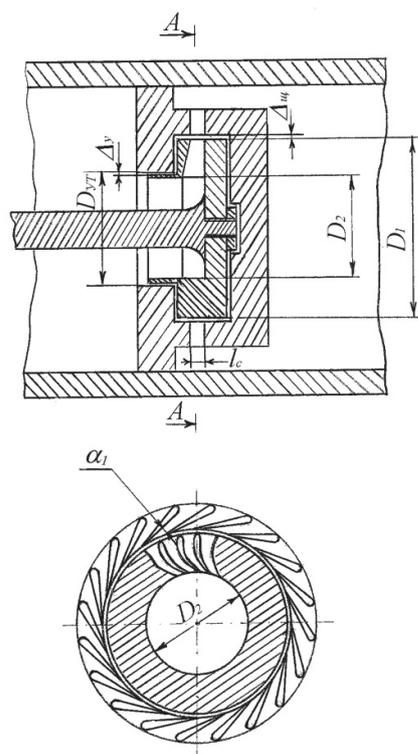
Схема центробежной турбины с частичным облопачиванием рабочего колеса
